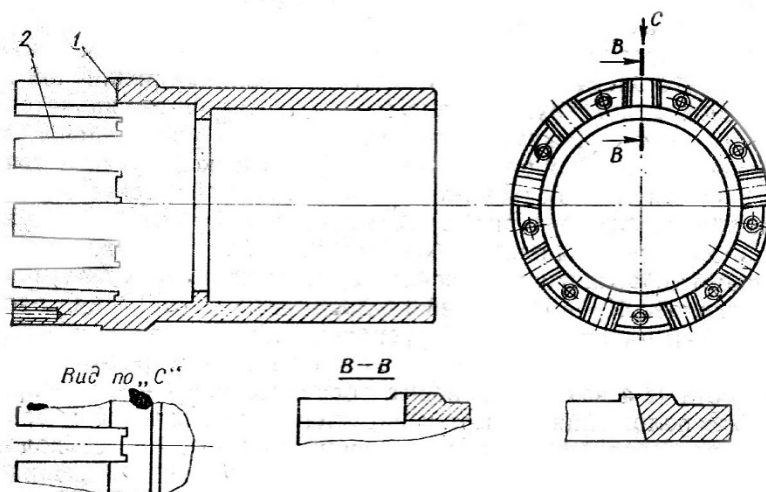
Корпус сепаратора: 1 – корпус сепаратора; 2 – бічні поверхні пазу
